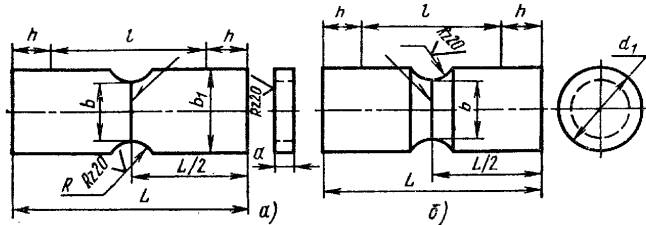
Образец для определения прочности металла шва в стыковом соединении при испытаниях сварного соединения на статическое растяжение
